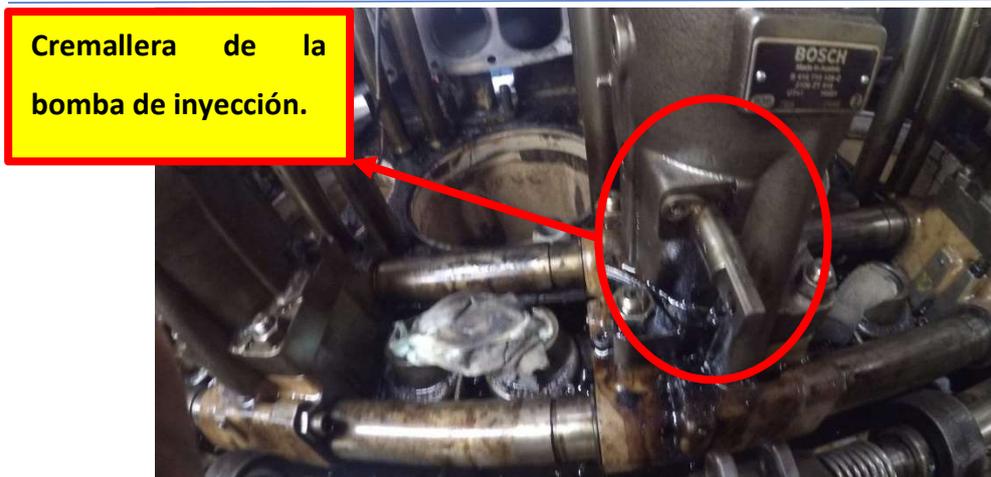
Detalle cremallera de la bomba de inyección. Fuente: Trabajo de campo.
